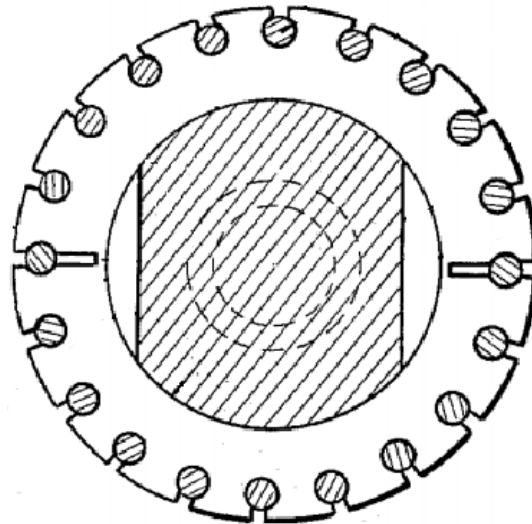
Vista da secção transversal de um rotor híbrido patenteado por F. W. Merrill [11].
